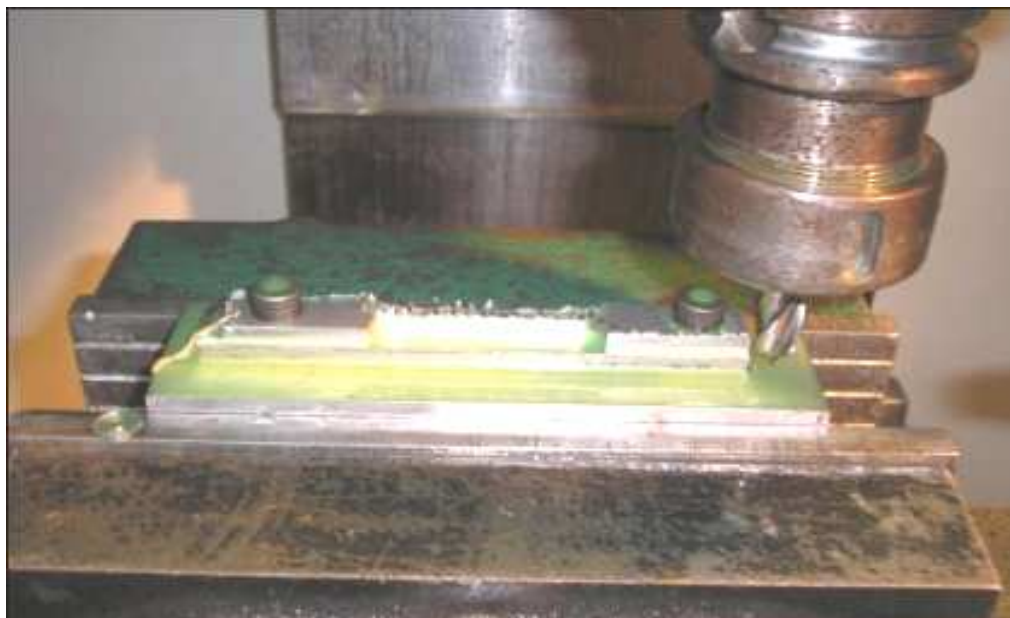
Corpo de prova usinado no centro de usinagem Fadal CNC 88HS da UNIFEL.
